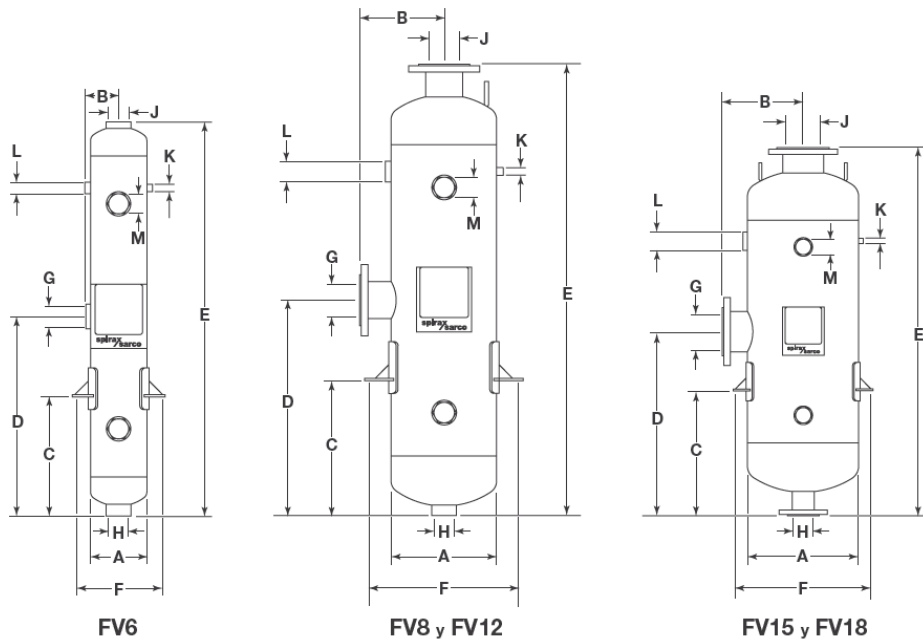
Esquema dimensional del tanque de revaporizado Spirax Sarco
